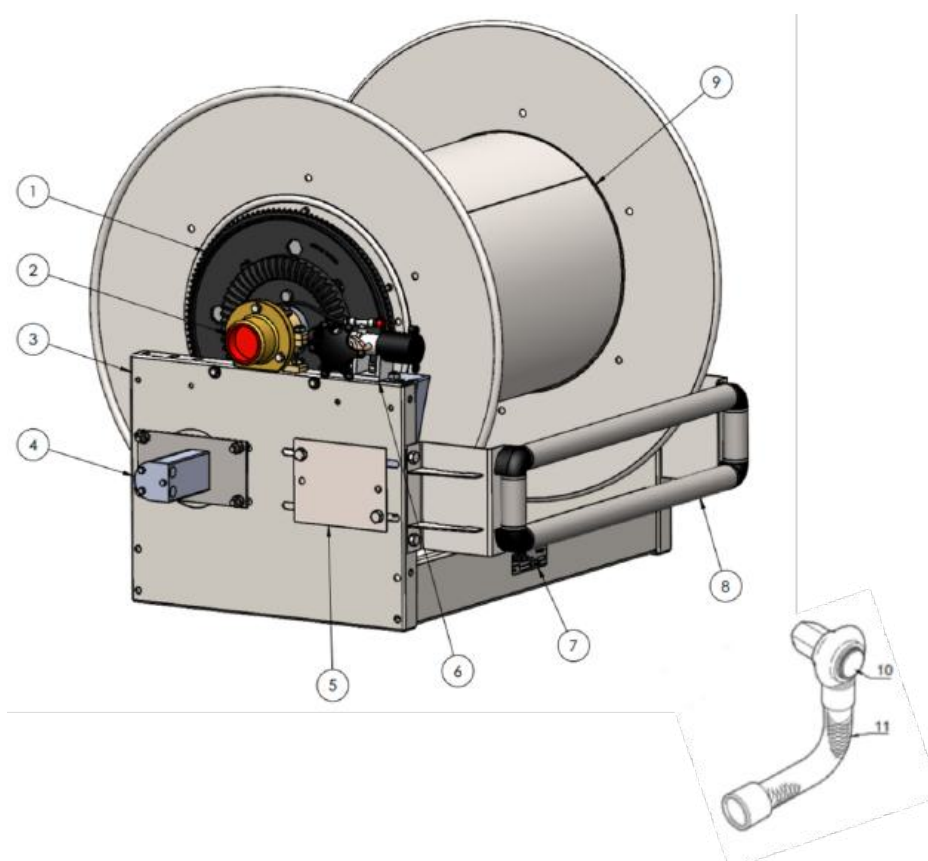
Enrollador de manguera de rebobinado con motor hidráulico (Protector de cadena desmontado)
